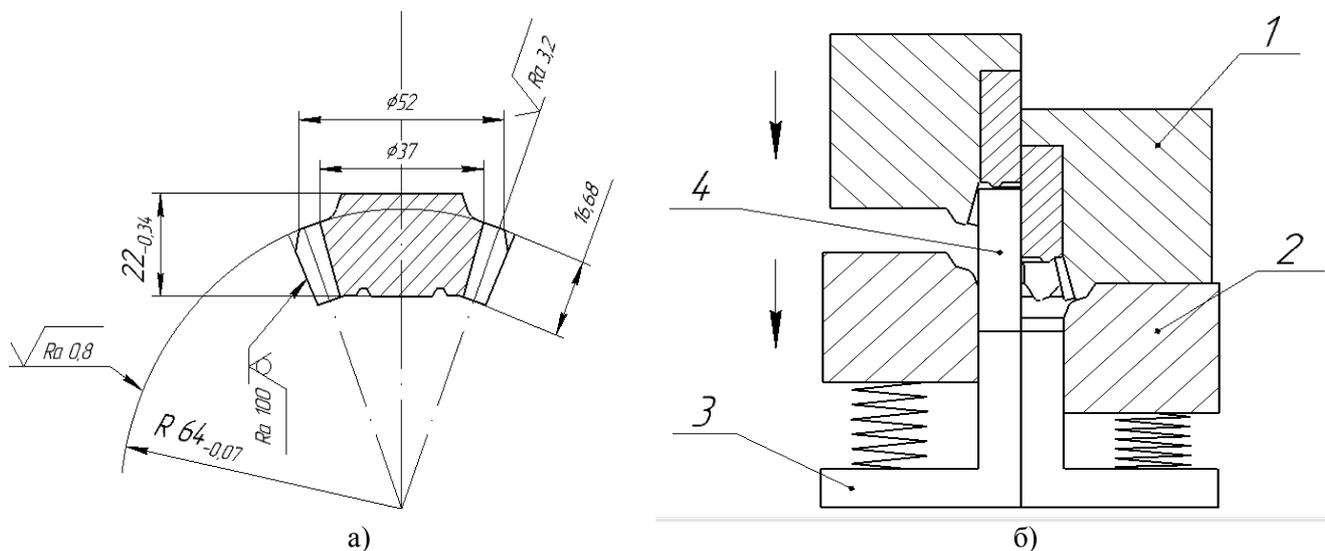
а) чертеж детали; б) схема штампа (1 – верхняя полуматрица, 2 – нижняя полуматрица, 3 – пуансон для выдавливания, 4 – заготовка)
